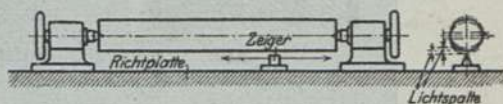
Prüfen runder Flächen nach dem Lichtspalt.
